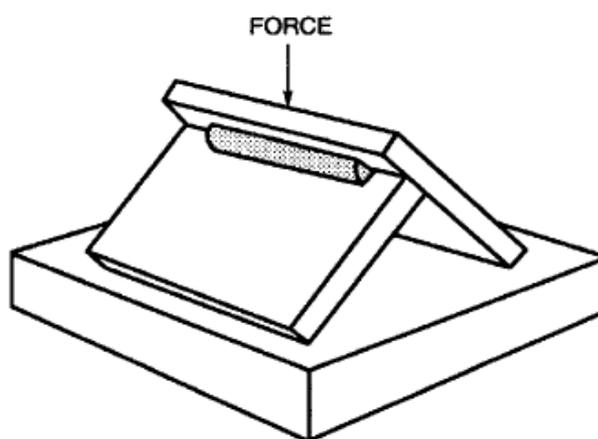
Cupón de prueba de ruptura para soldador de puntos.
